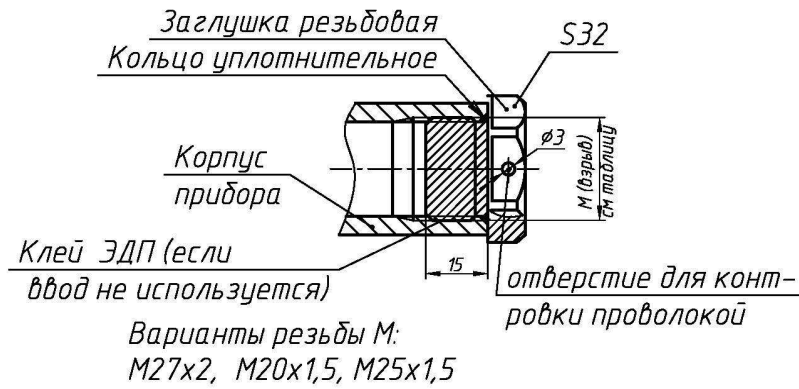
Элементы взрывозащиты при поставке извещателя с резьбовыми заглушками
